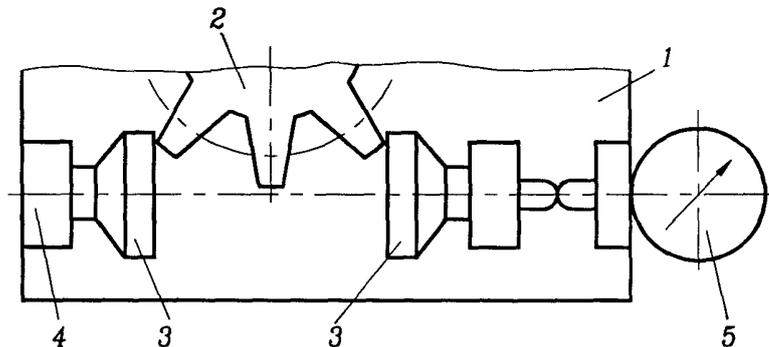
Схема контроля средней длины общей нормали: 1 – корпус; 2 – зубчатое колесо; 3 – наконечник; 4 – стойка; 5 – индикатор
